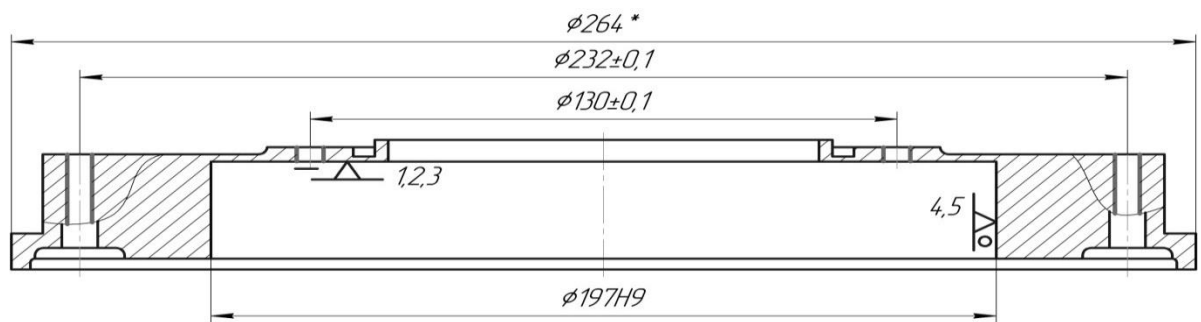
Схема базування заготовки на жорсткій оправці
